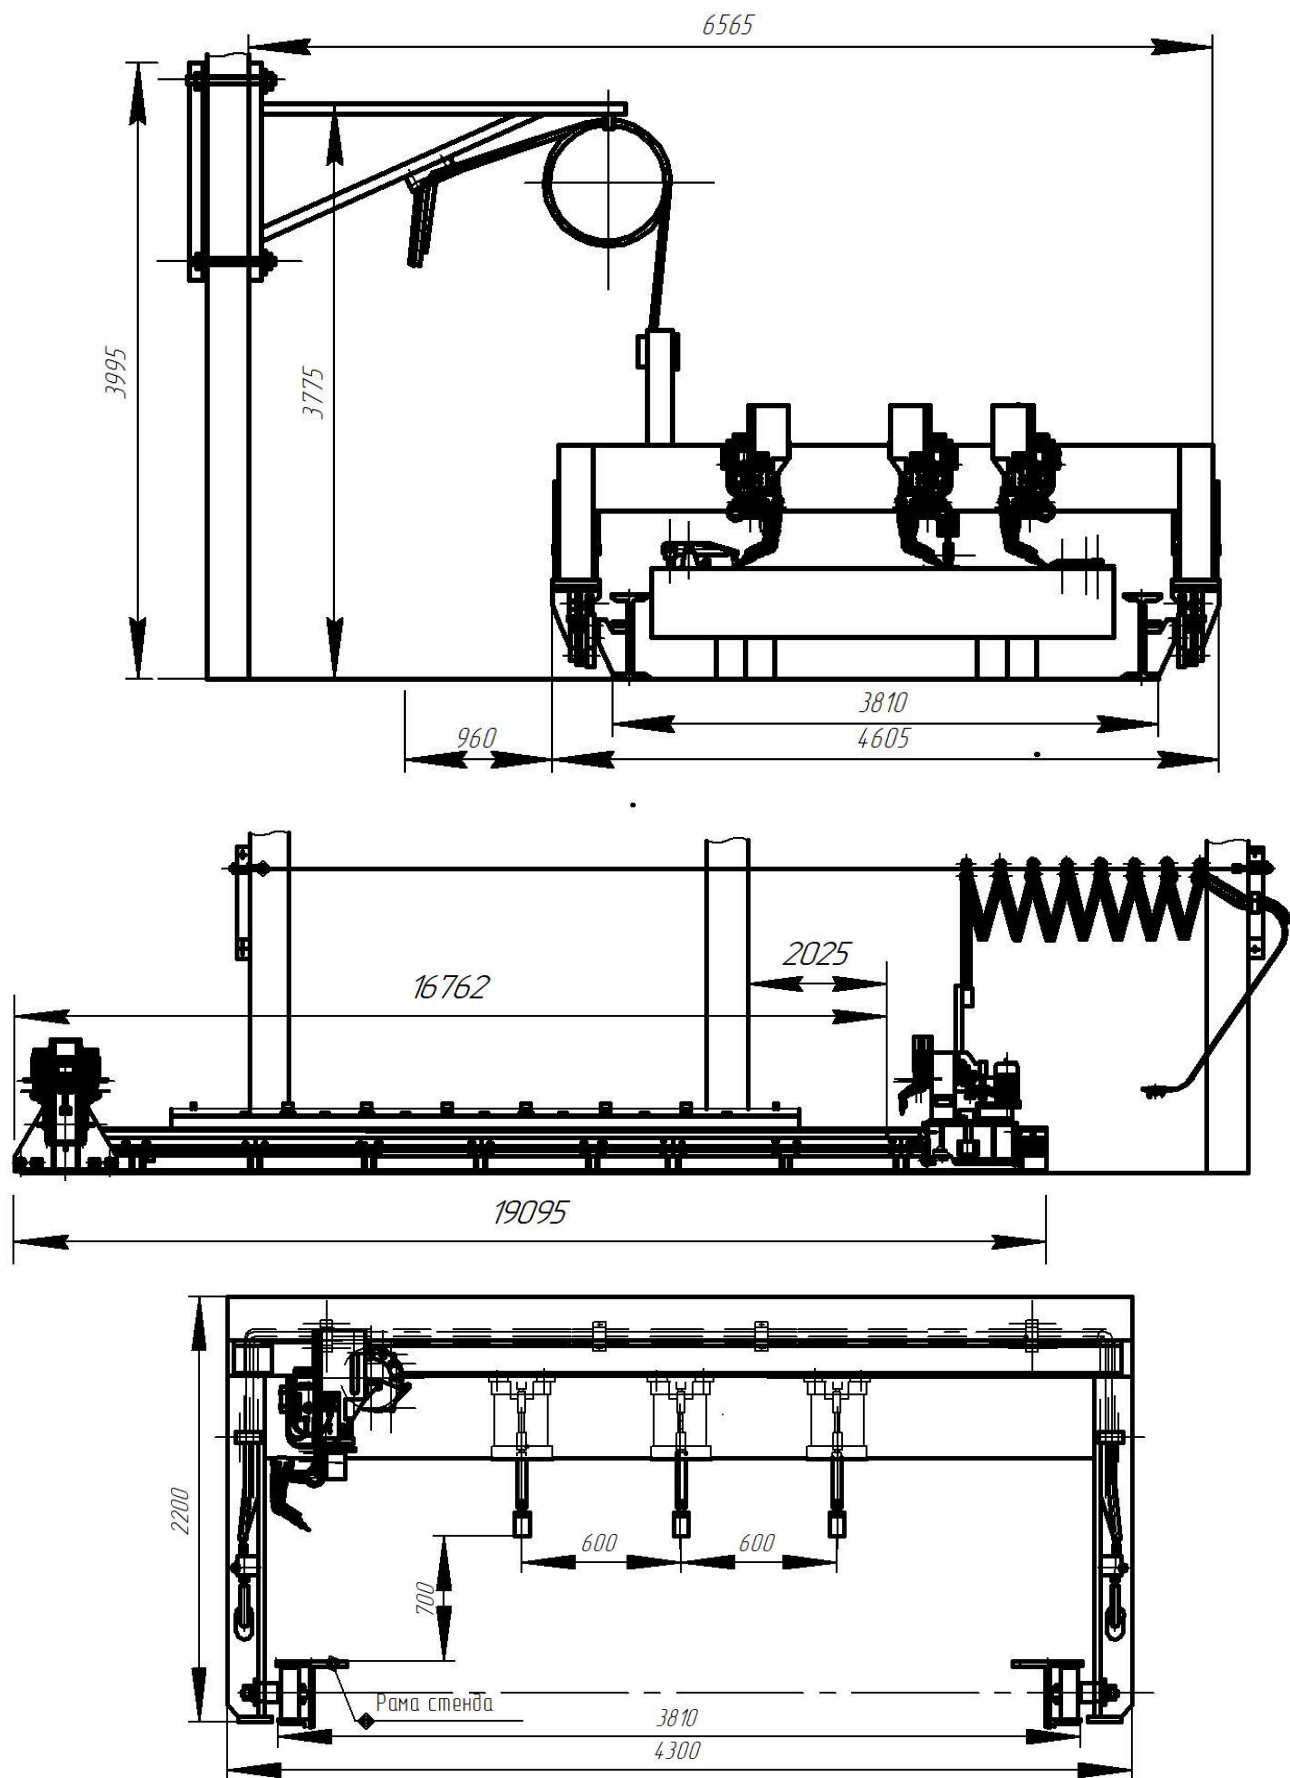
Загальний вигляд установки для складання та зварювання
